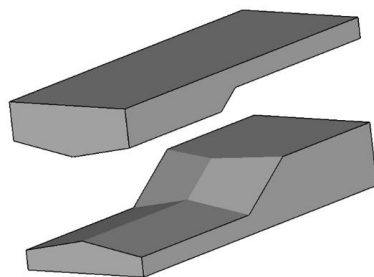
Новая конструкция ступенчато-клиновых бойков
